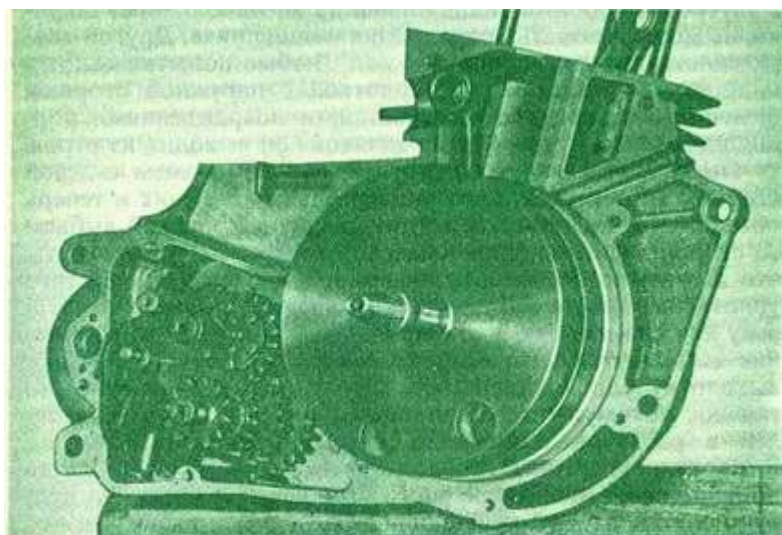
Левая половина картера с коробкой передач и кривошипно-шатунным механизмом
